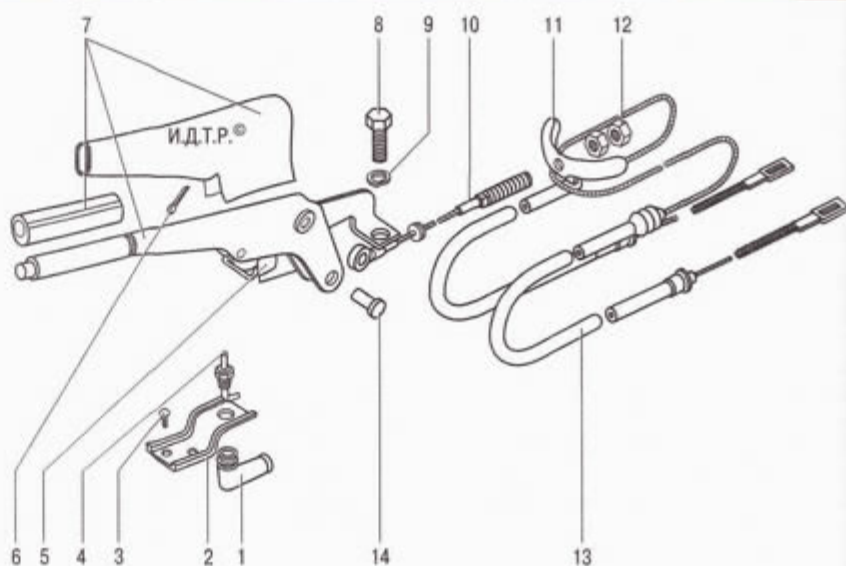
Детали привода стояночного тормоза: 1 – защитный колпачок; 2 – кронштейн; 3 – выключатель контрольной лампы включения стояночного тормоза; 4 – упор; 5 – шплинт; 6 – болт; 7 – шайба; 8 – передний трос привода стояночного тормоза; 9 – уравниватель; 10 – гайка; 11 – задний трос привода стояночного тормоза; 12 – палец
